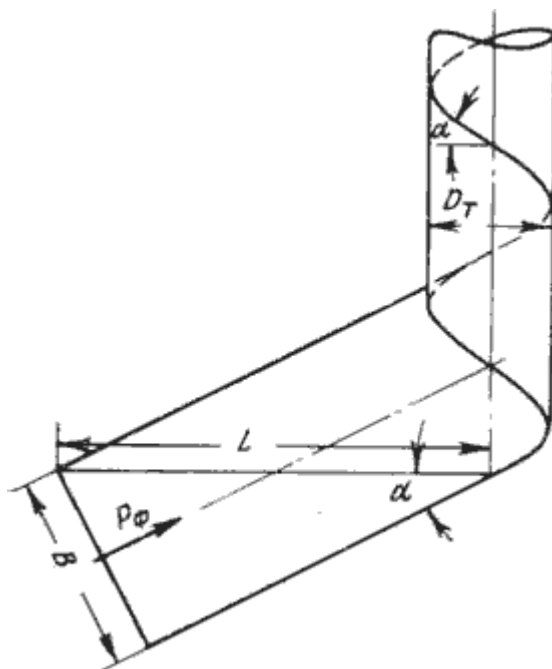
Схема формовки заготовки при спиральной сварке трубы
